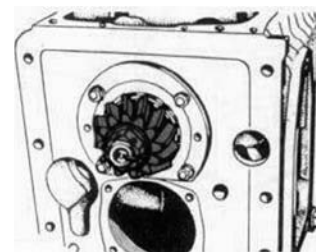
Снятие ведущей шестерни глав нойпередачи для ее замены или регулировки ее установочной высоты
